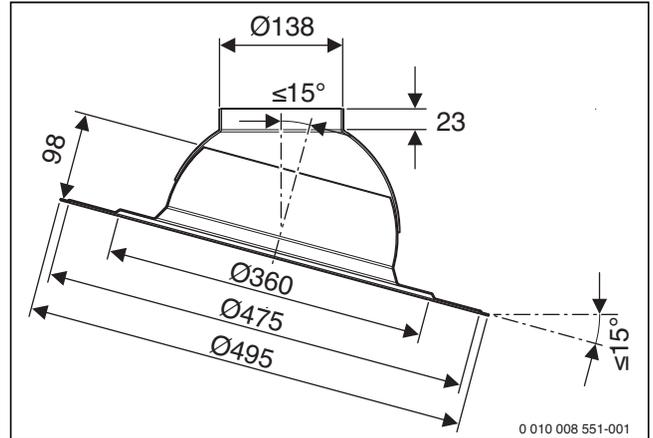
Flachdach-Klebeflansch für DN 80/125 (Maße in mm)
